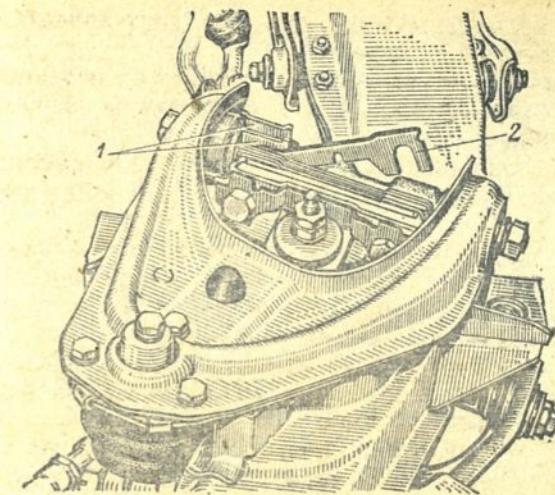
Узел регулировки угла продольного наклона поворотной стойки подвески и угла развала переднего колеса:
